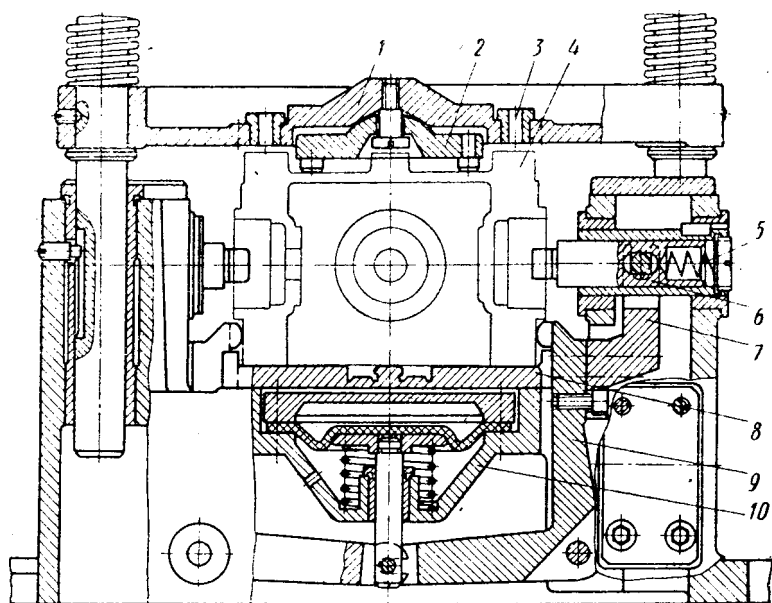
Приспособление к многошпindleйной головке для обработки отверстий в корпусных деталях
